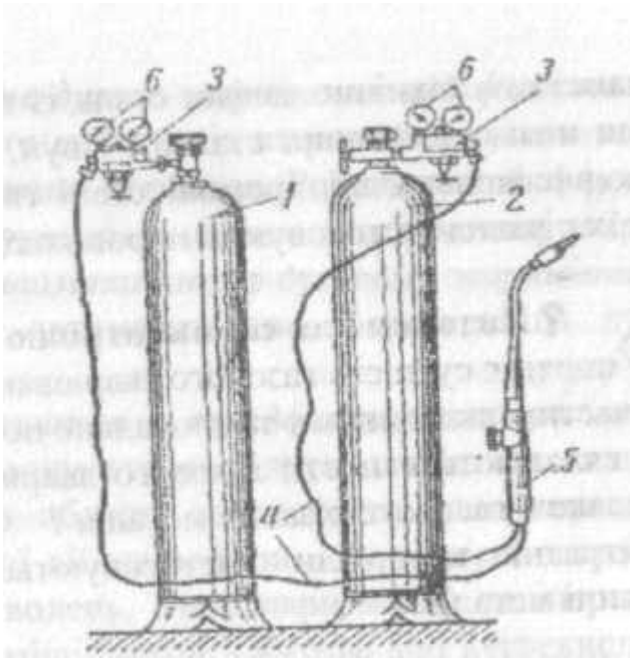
Газозварювальна установка з кисневим і ацетиленовим балонами: 1 - кисневий балон; 2 - ацетиленовий балон; 3 - редуктори; 4 - гумові рукави; 5 - зварювальний пальник; 6 -- манометри
